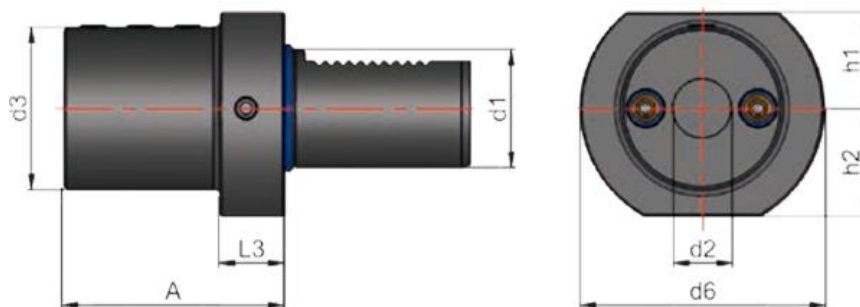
Оправка VDI40 для інструменту з хвостовиком типу Weldon E2-40x40
